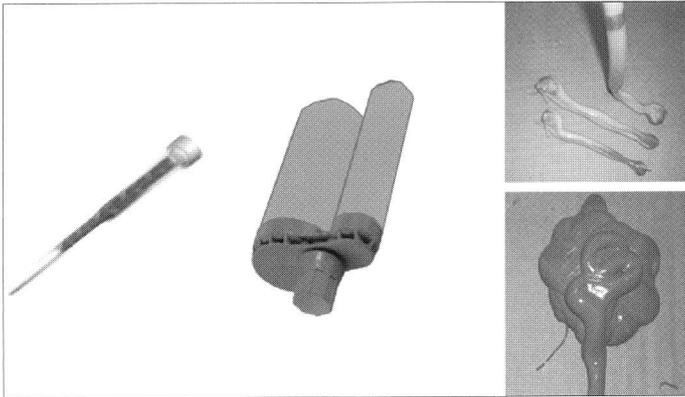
(a) Detalle de la boquilla mezcladora y de los dos componentes de un adhesivo. Se puede apreciar que en este caso, los componentes no se mezclan en partes iguales. (b) Arriba, adhesivo que sale inicialmente de la boquilla en el cual aún no se han mezclado bien los componentes. Abajo, adhesivo bien mezclado (Meinheit, 2014).
